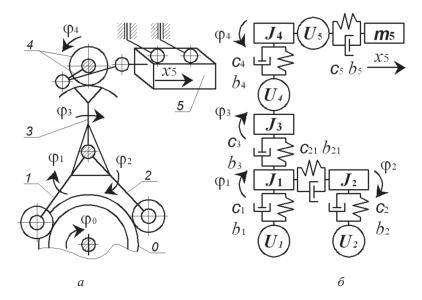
Кулачково-рычажный привод механизма переноса XBA 1818 (а) и его динамическая модель (б): 0 — блок кулаков; 1 — рычаг прямого хода; 2 — рычаг обратного хода; 3 — верхнее плечо рычага прямого хода с зубчатым сектором; 4 — кривошип с зубчатым колесом; 5 — каретка переноса
